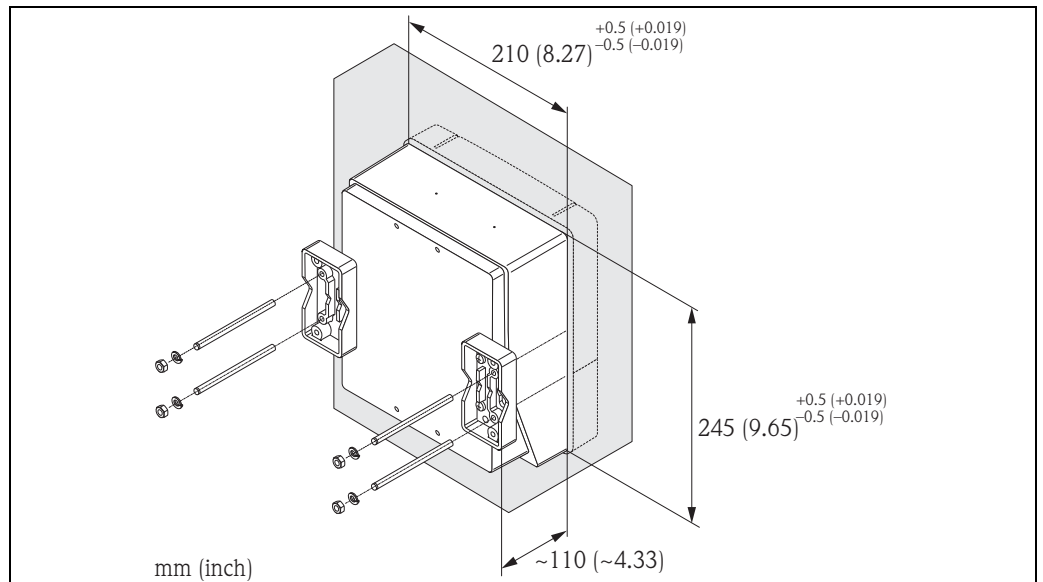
Установка панели (корпус, предназначенный для настенного монтажа)
